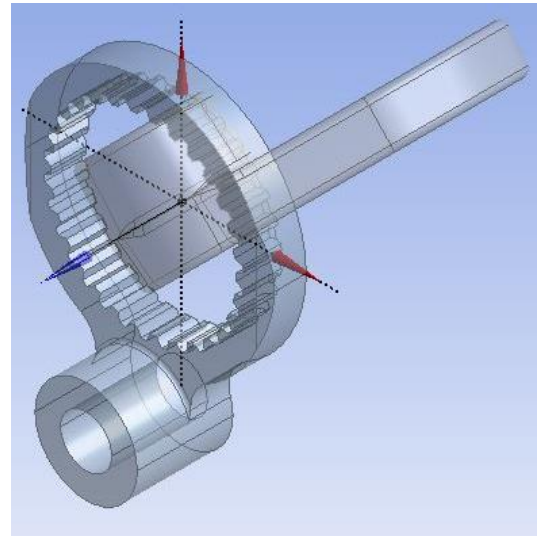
Початкове розташування CAD моделей заготовки та деталі в тестовій задачі
